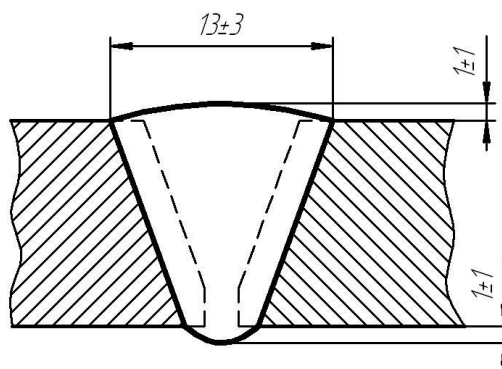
Геометрия сварного шва при заварке трещины
